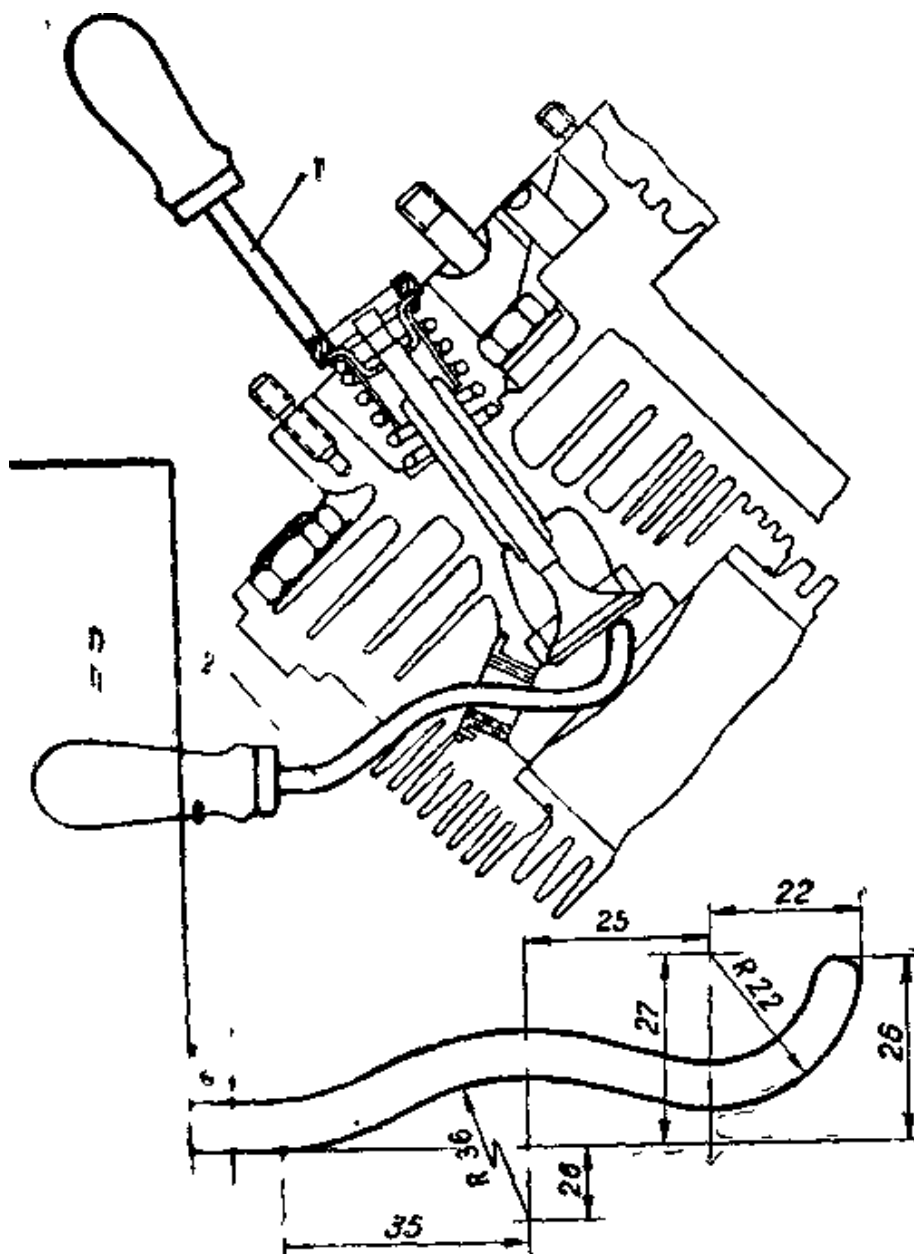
Приспособление для снятия пружины клапана без разборки двигателя
